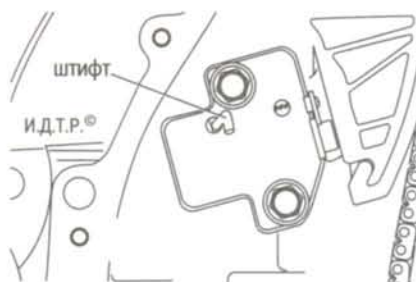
Фиксация натяжителя цепи привода газораспределительного механизма
